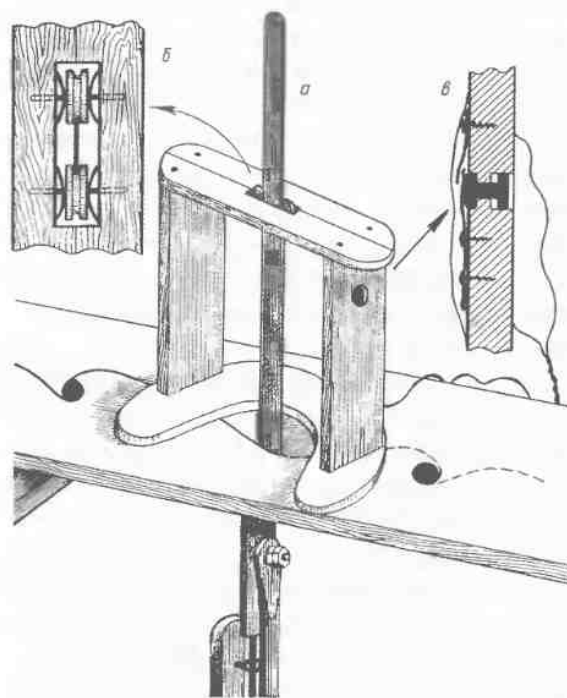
Кондуктор механического лобзика: а — общий вид; б — вид сверху на направляющие ролики; в — выключатель
